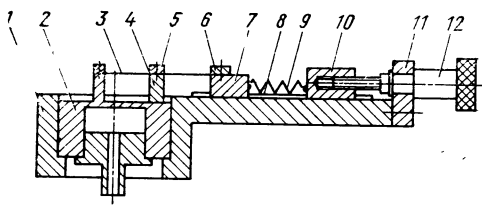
Схема приспособления для регулировки начальной частоты колебаний струнного преобразователя
